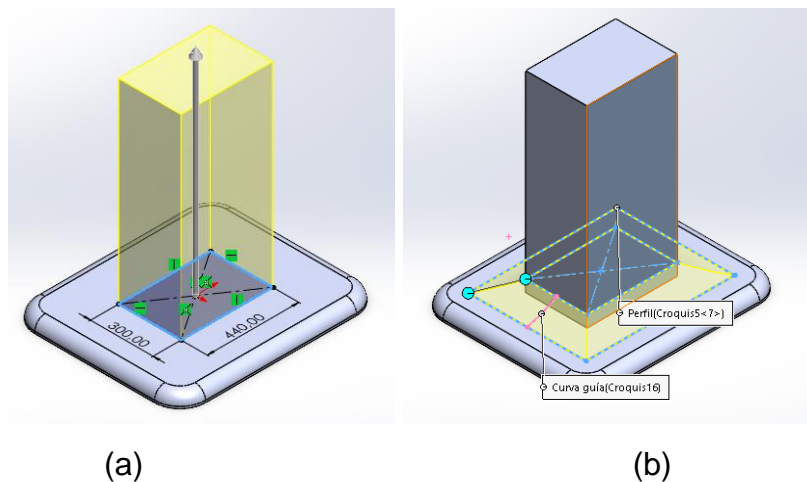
(a) Extrusión cuerpo en SolidWorks. (b) Recubrimiento base en SolidWorks.
